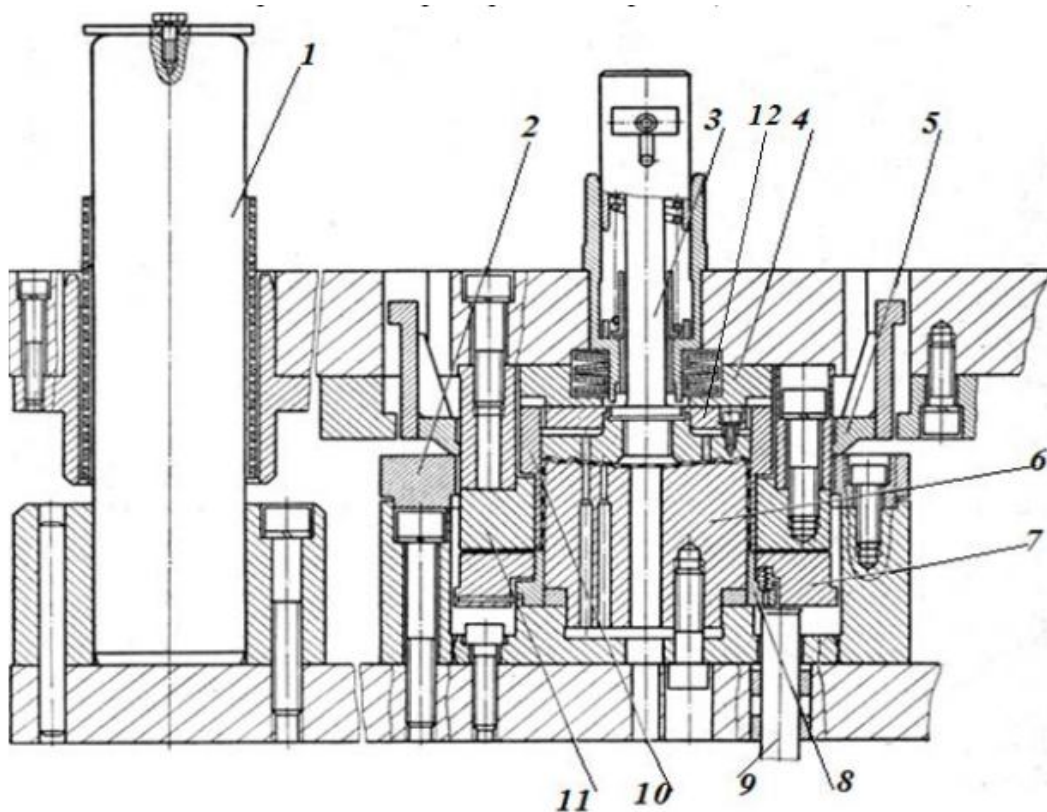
Комбінований штамп для глибокої витяжки жерстяних банок: 1 - пакет штампа з направляючими колонками; 2 - ріжуче кільце;
